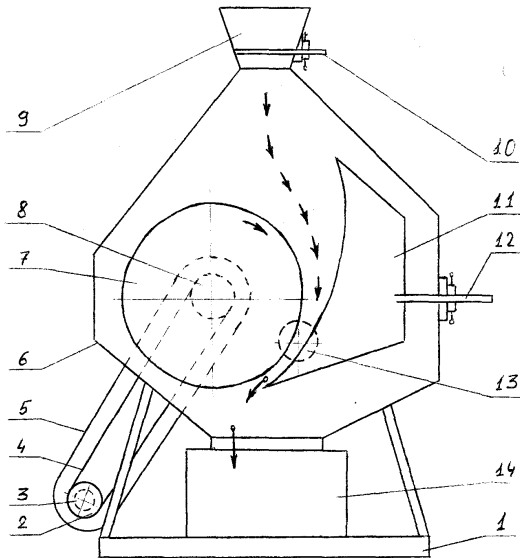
Гречерушальний верстат: 1 - рама; 2 - електродвигун; 3 - шків (вала електродвигуна); 4 - клиновий пас; 5 - захисний кожух; 6 - корпус; 7 - активний робочий орган (абразивний циліндр (диск)); 8 - шків (вала активного робочого органу); 9 - бункер для нешелушеного зерна гречки; 10 - механізм регулювання подачі зерна гречки; 11 - пасивний робочий орган (гумовий шелушитель); 12 - механізм регулювання зазору між активним й пасивним робочими органами (між абразивним циліндром (диск) і гумовим шелушительником); 13 - лючок (у корпусі) для установки зазору між активним й пасивним робочими органами; 14 - прийомний бункер для продукту (суміші, отриманої в процесі шелушіння);  $\curvearrowright$  - напрямок обертання активного робочого органу;  $\leftarrow$  - напрямок руху подаваного для шелушіння зерна гречки;  $\leftarrow$  - напрямок руху продукту, що одержується у процесі шелушіння
